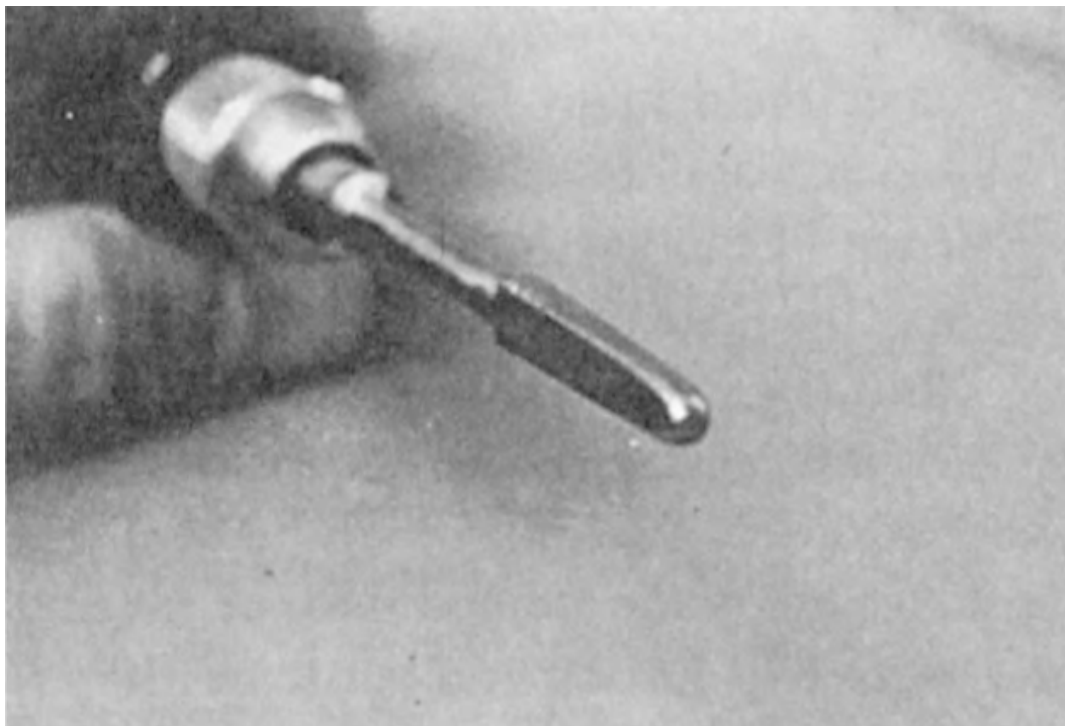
Детальний знімок інструмента для розширення отвору балансної рейки
